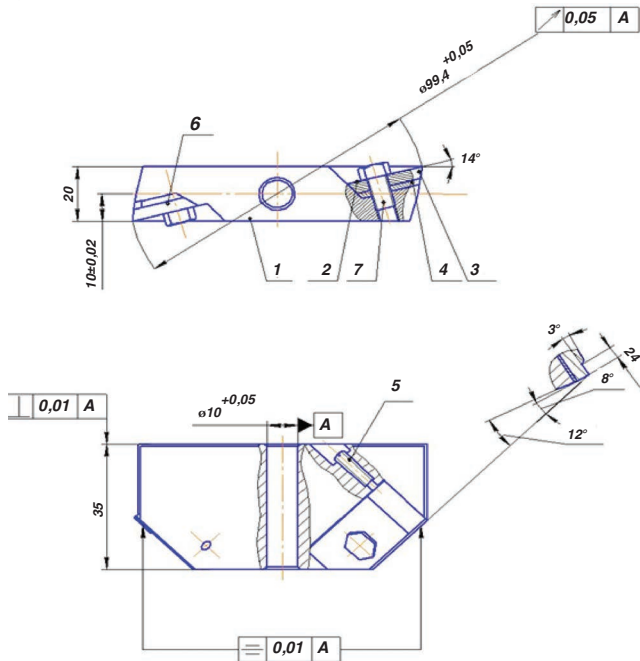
Блок режущий с механическим креплением раздвижных твердосплавных пластин: 1 — корпус; 2 — клин; 3, 6 — пластина твердосплавная; 4 — подложка; 5 — винт; 7 — болт.
